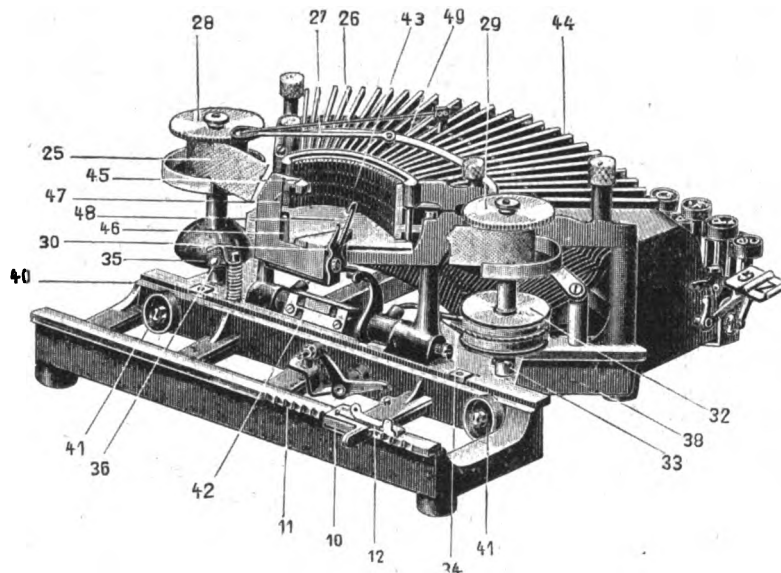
Z. A.: „Adler“-Schnell-Schreibmaschine.
